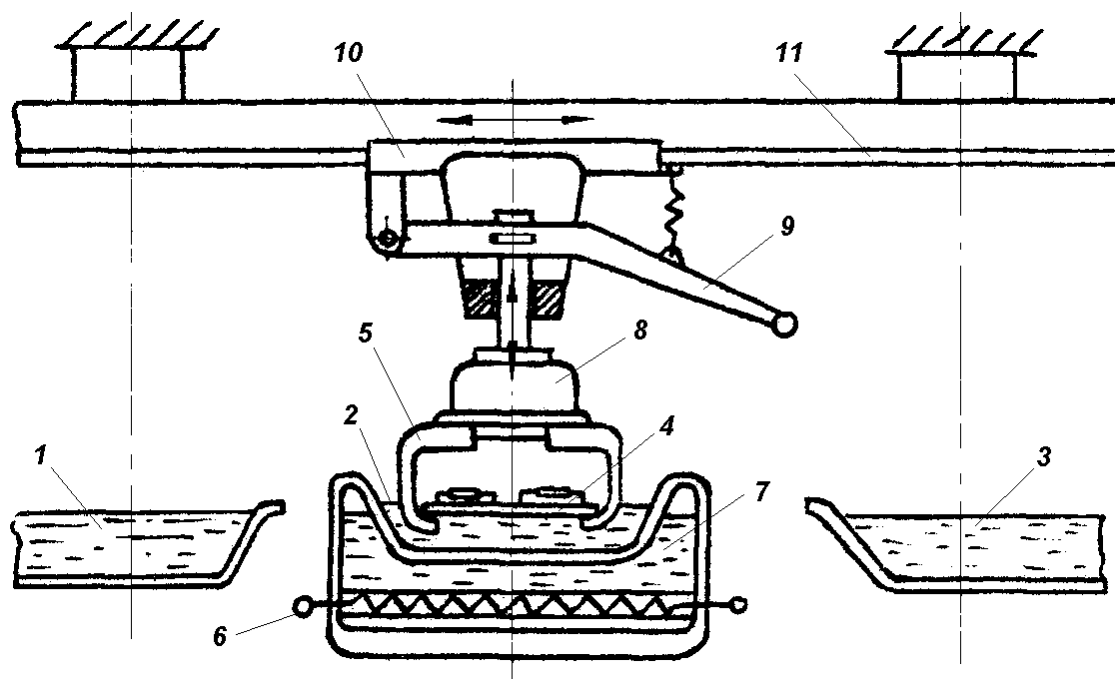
Схема установки для пайки погружением: 1 – ванна с флюсом; 2 – ванна с припоем; 3 – ванна для отмывки маски и остатков флюса; 4 – плата; 5 – приспособление для крепления платы; 6 – электронагреватель; 7 – соляная ванна; 8 – вибратор; 9 – рычаг; 10 – каретка; 11 – направляющие каретки
